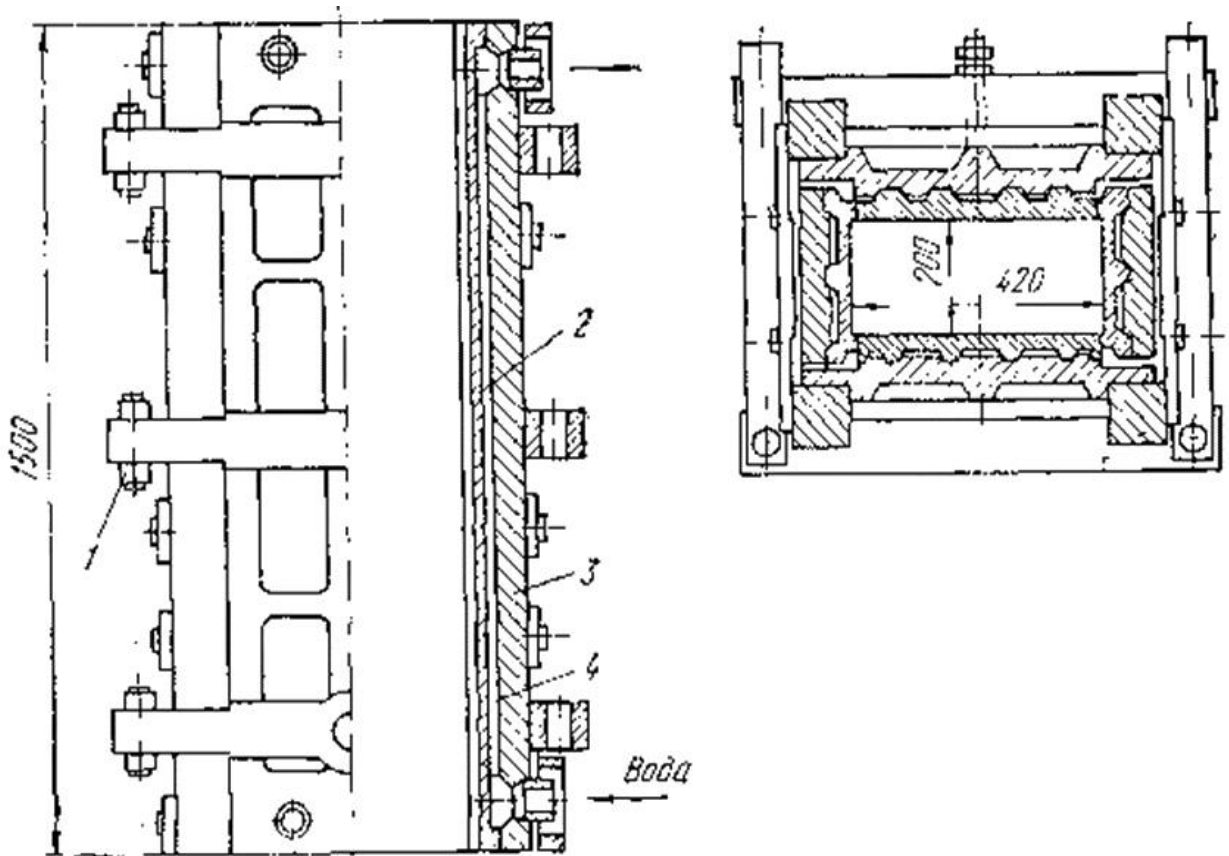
Кристалізатор машини безперервної розливки сталі: 1 – елементи для з'єднання, 2 – мідна пластина; 3 – сталевий корпус кристалізатора; 4 – зазор для подачі рідини
